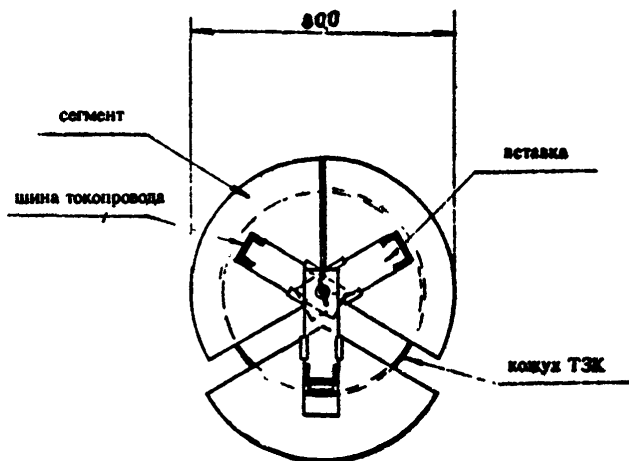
Торцевая заглушка для защиты изоляторов токопровода ТЗК при сварке блоков в вертикальном положении
